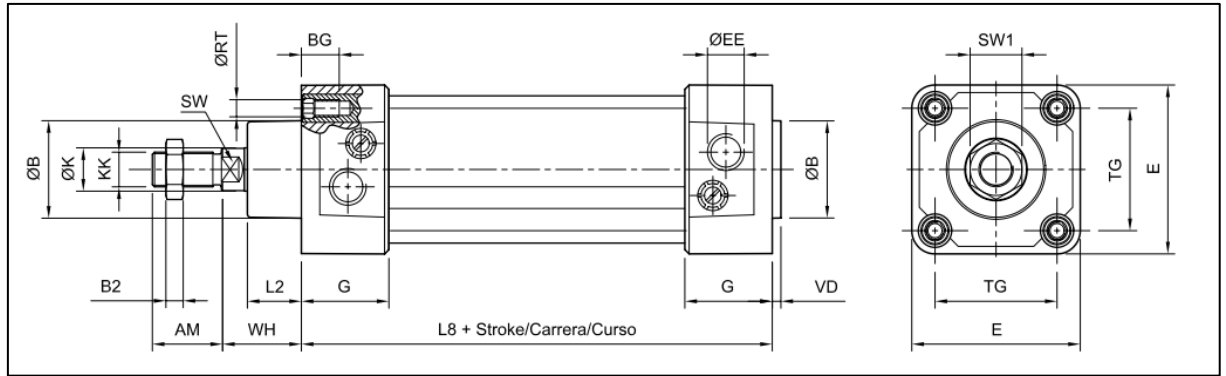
Desenho com principais dimensões do cilindro de força 1 [20].
